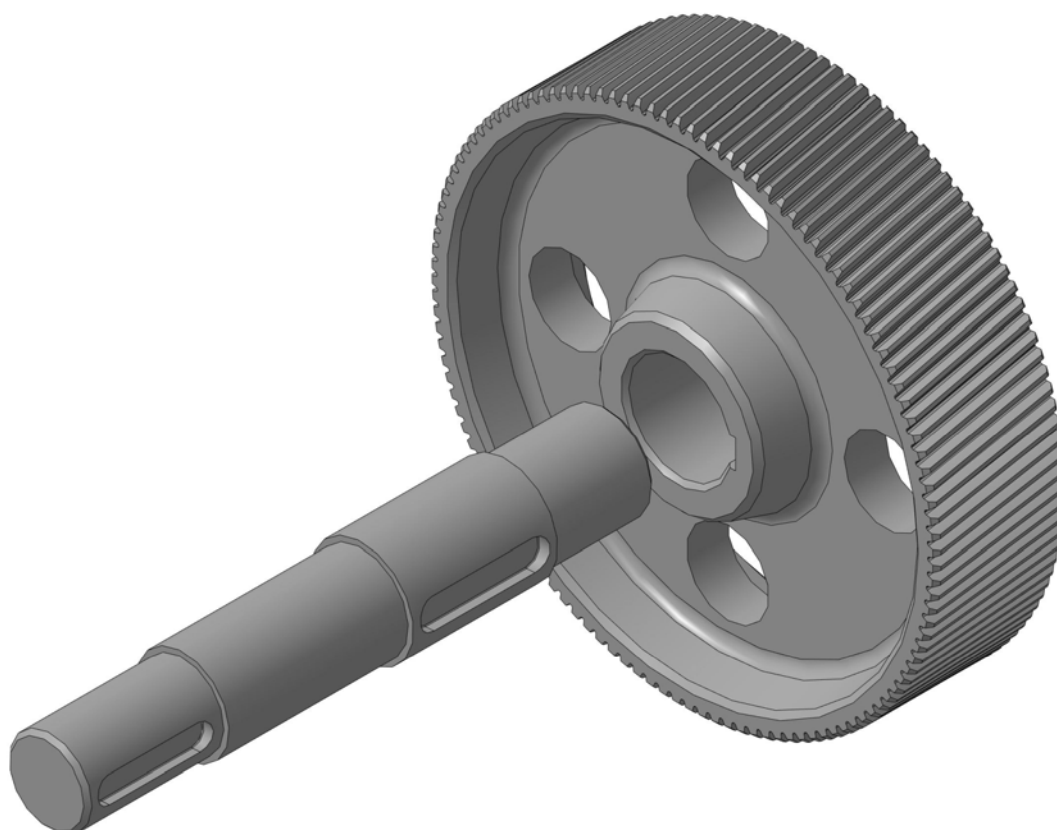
Cad-модель веденого (тихохідного) вала у зборі з циліндричним колесом
